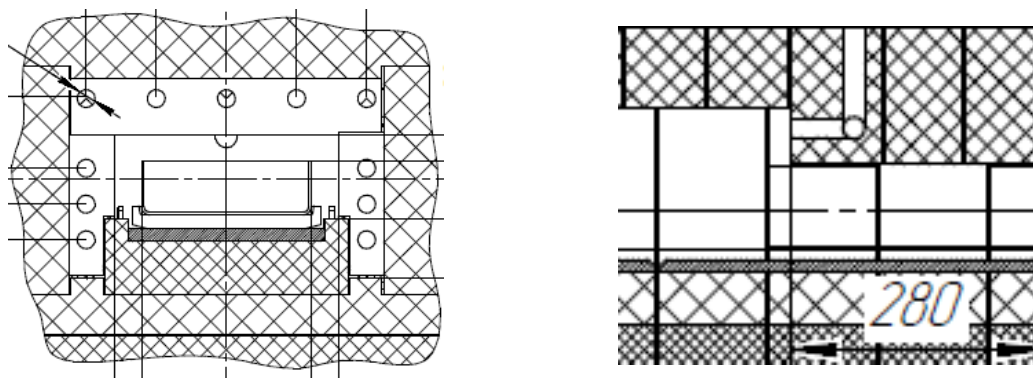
эскиз конструкции газового барьера проходной печи
